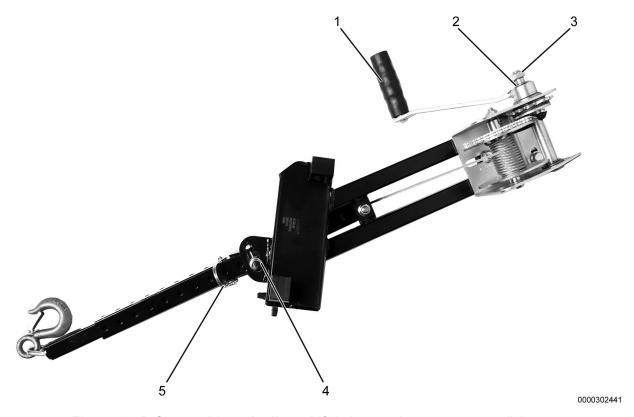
Pré-assemblage du dispositif de levage du compresseur d'air.
